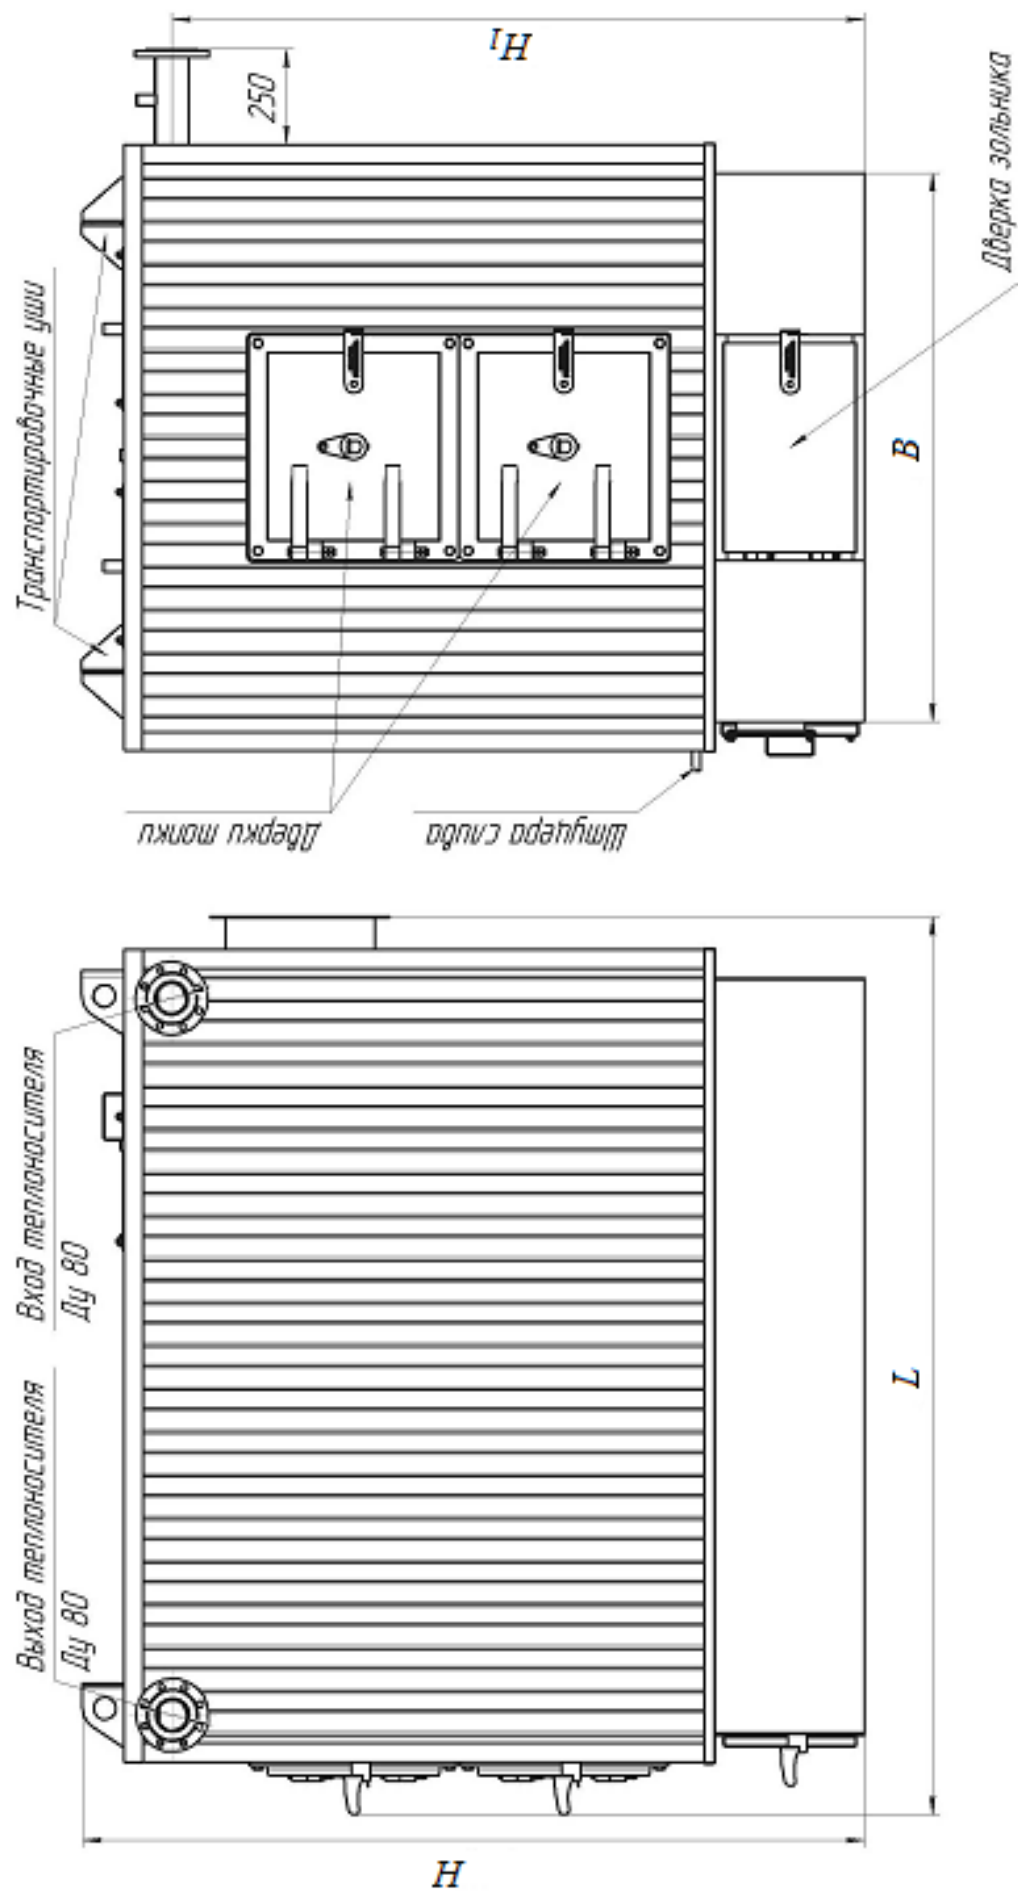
а. Габаритные и присоединительные размеры котла КВр.
